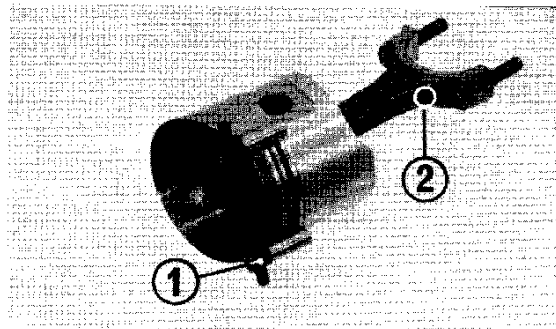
(1) Kolbenring-Einführwerkzeug
